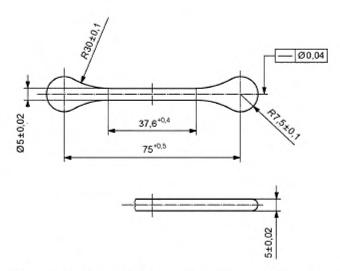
Эскиз полости пресс-формы для изготовления образцов-свидетелей для испытаний на растяжение типа В
